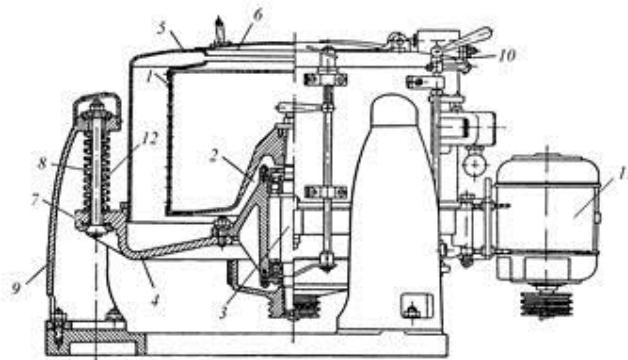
Триколонна центрифуга: 1 – ротор; 2 – конус; 3 – вал; 4 – днище; 5 – кожух; 6 – кришка; 7 – станина; 8 – тяга; 9 – колонна; 10 – гальмо; 11 – двигун; 12 – пружина
